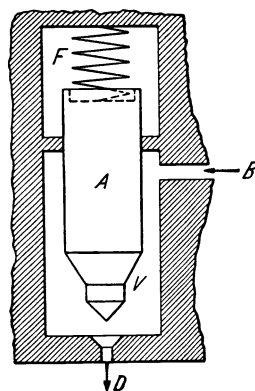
Aufbau eines Einspritzventils für Ölmotoren.
